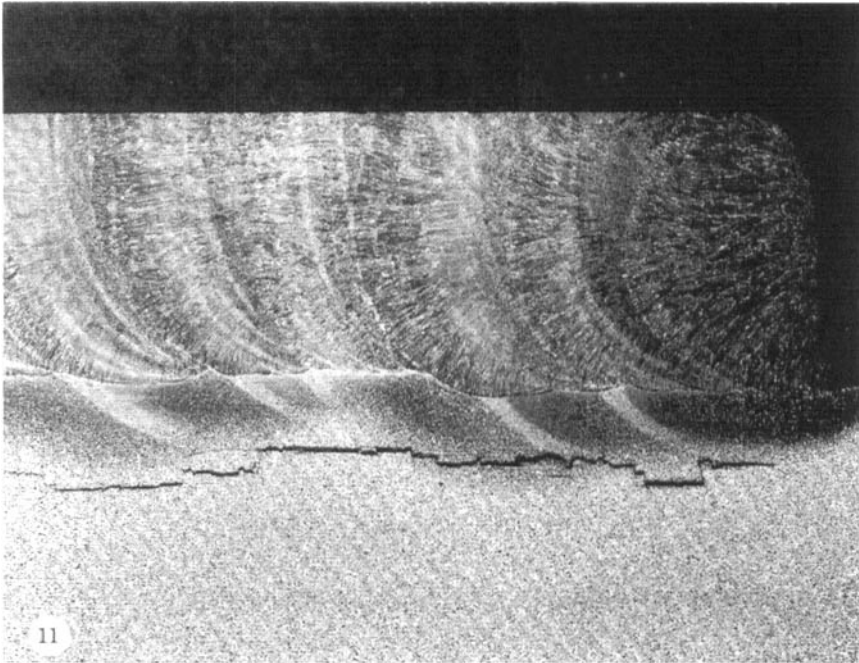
Fissuration par arrachement lamellaire sur une soudure.
